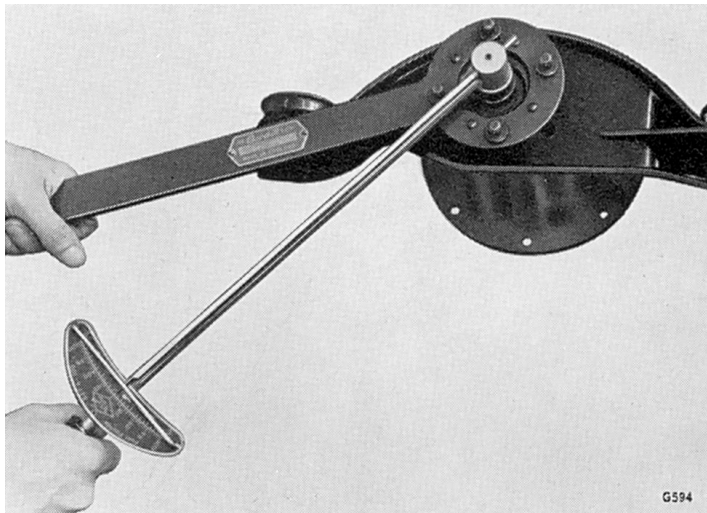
Serrage de l'écrou de bride d'entraînement du pignon d'attaque
